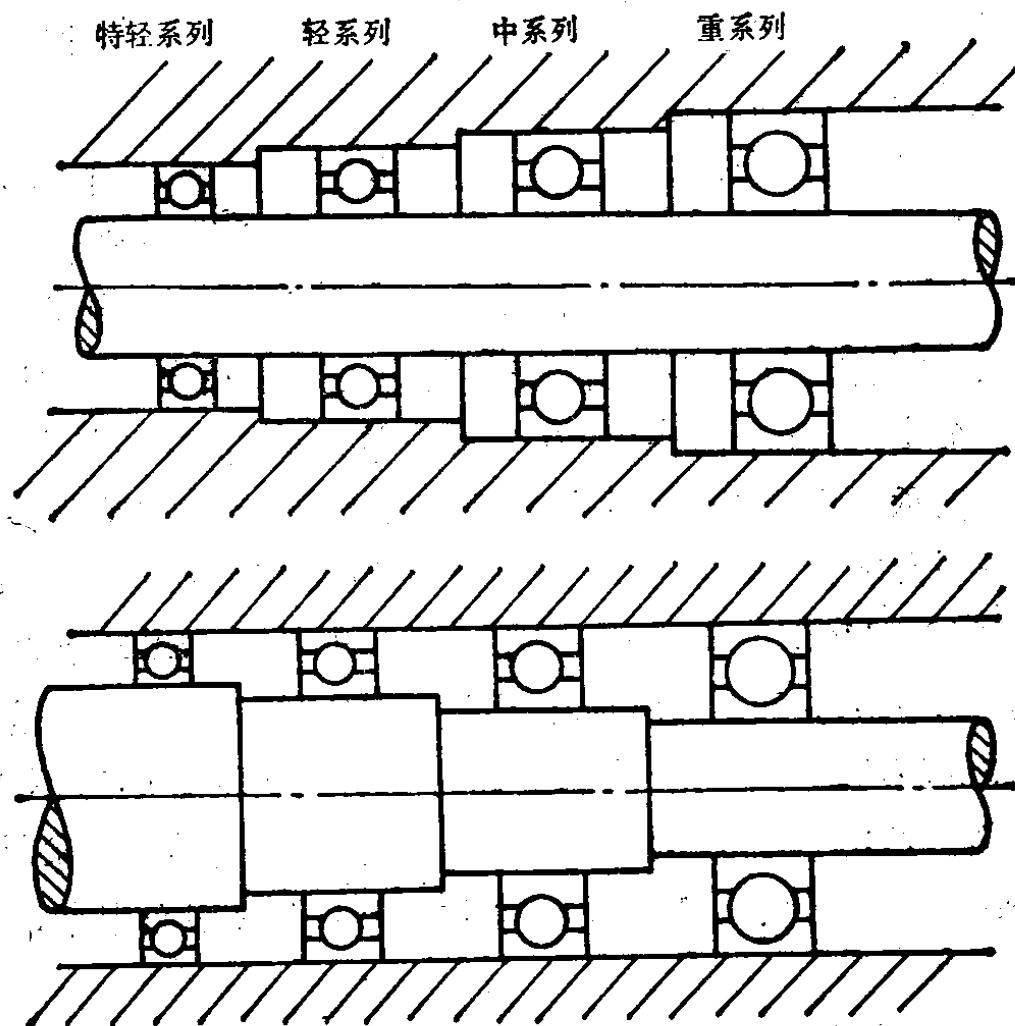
轴承尺寸的标准带来了使用者选用轴承时的巨大灵活性
